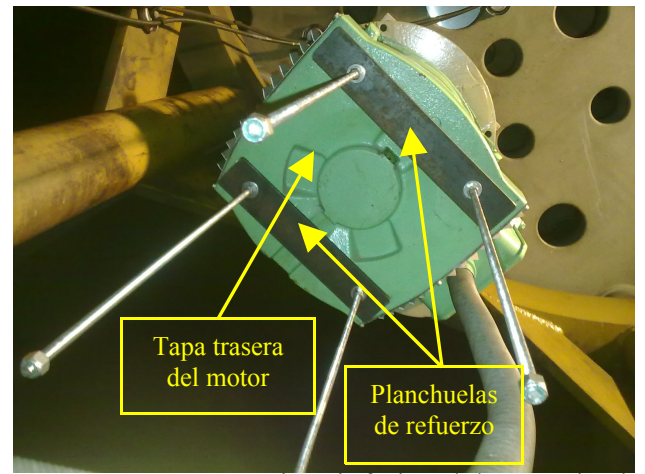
Vista inferior del montaje del motor del RS CB1
